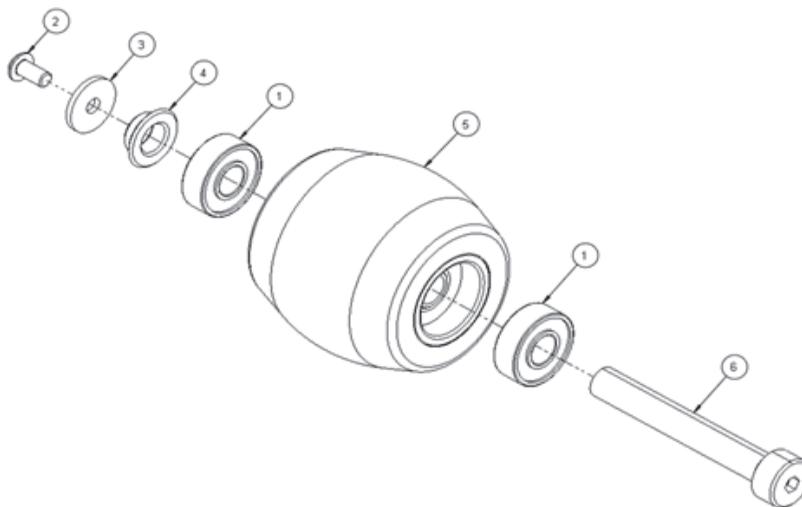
Vue éclatée – Roue magnétique – Q8301797
